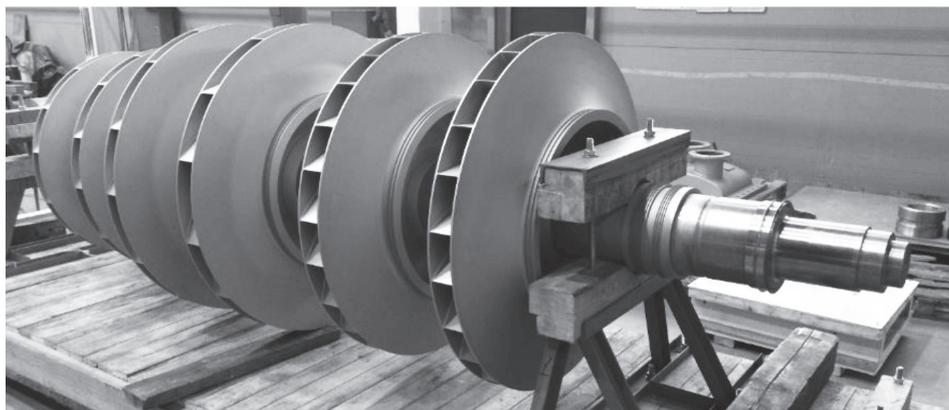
Модернизированный ротор компрессора типа К1500-62-2
